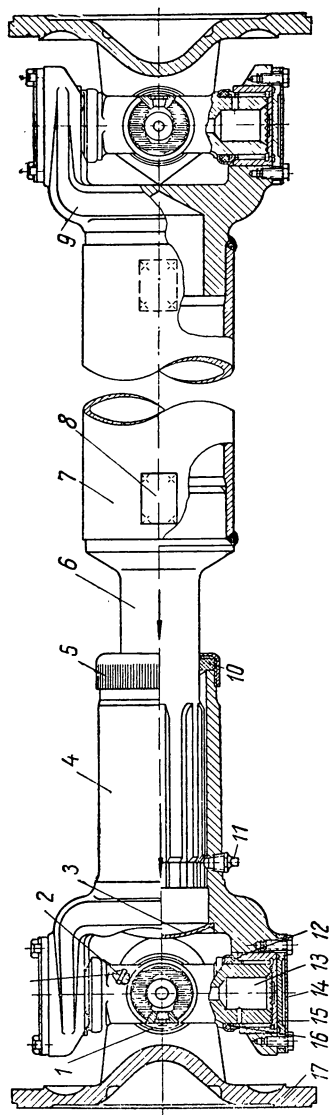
Карданный зал заднего моста: 5 — обойма сальника скользкой вилки; 4 — скользящая вилка; 8 — игольчатый подшипник; 12 — игольчатый подшипник; 13 — иглообразный подшипник; 14 — стопорная пластина; 10 — задний вал; 6 — шлицевый конец; 7 — труба карданного вала; 8 — балансировочная пластина; 9 — вилка; 10 — уплотнительное кольцо; 11 — масленка; 12 — игольчатый подшипник; 13 — иглообразный подшипник; 14 — стопорная пластина; 15 — крышка игольчатого подшипника; 16 — сальник; 17 — фланец-вилка
